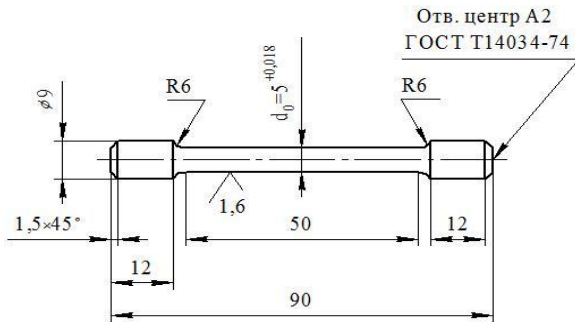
Циліндричний зразок для випробування на статичний розтяг
